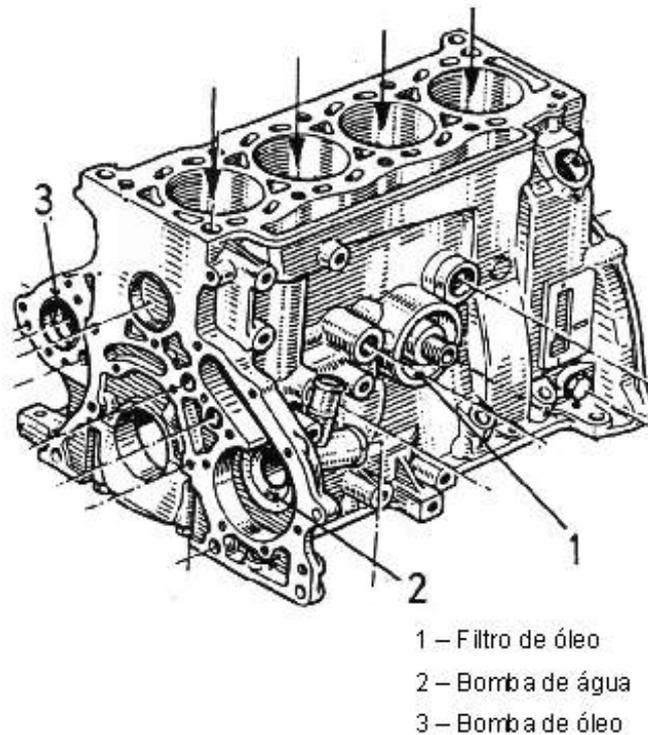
Inspeccionar zonas de fixação de componentes do bloco
